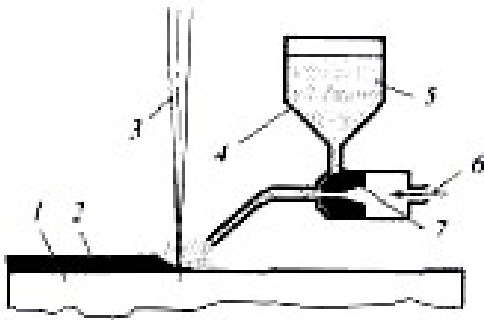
Схема процесса наплавки с подачей порошка газовой струей:
